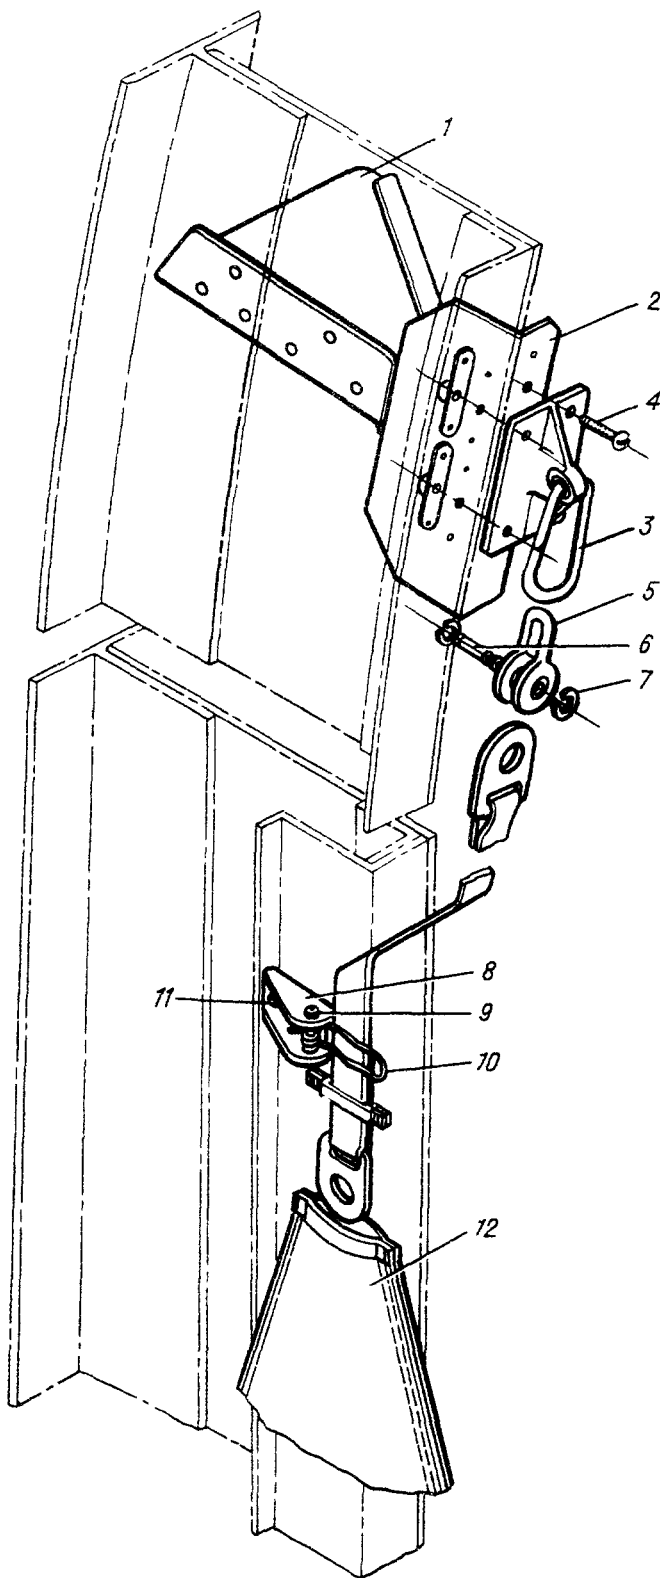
УСТАНОВКА КОЛЬЦА ДЛЯ ВЫПУСКАЮЩЕГО
